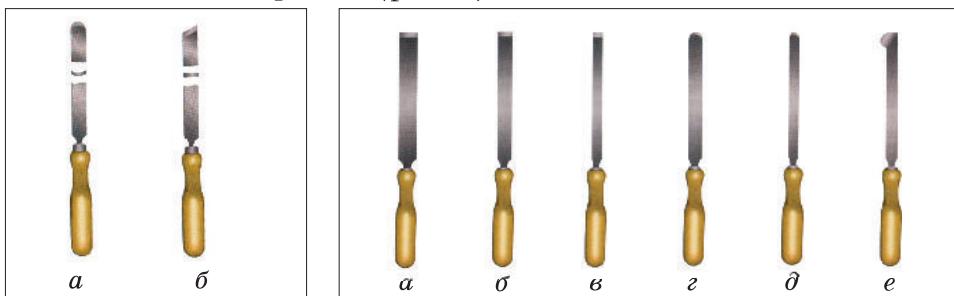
Режущий инструмент: а – полукруглая стамеска; б – косая стамеска
